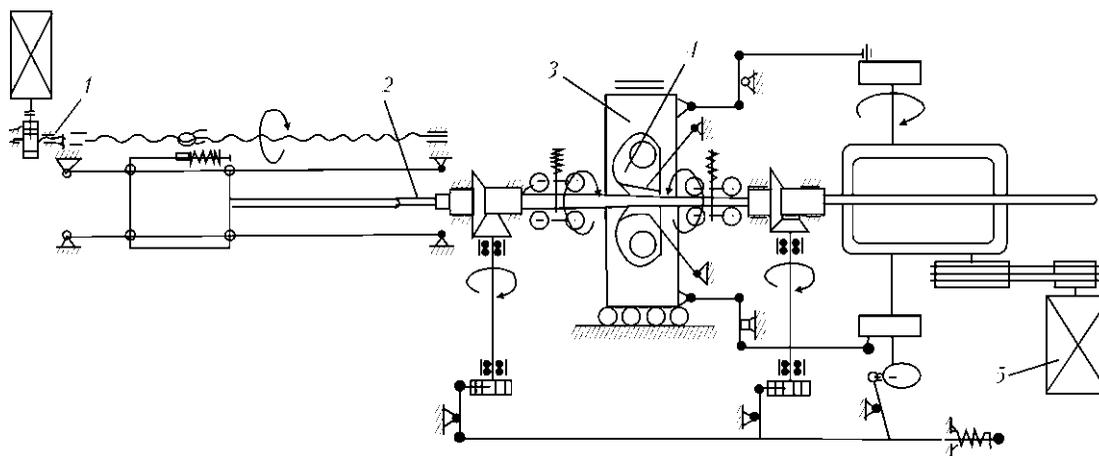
Кинематическая схема стана: 1 – привод механизма подачи; 2 – толкатель задающего устройства; 3 – прокатная клеть; 4 – валки; 5 – электродвигатель главного привода стана прокатной клетки
